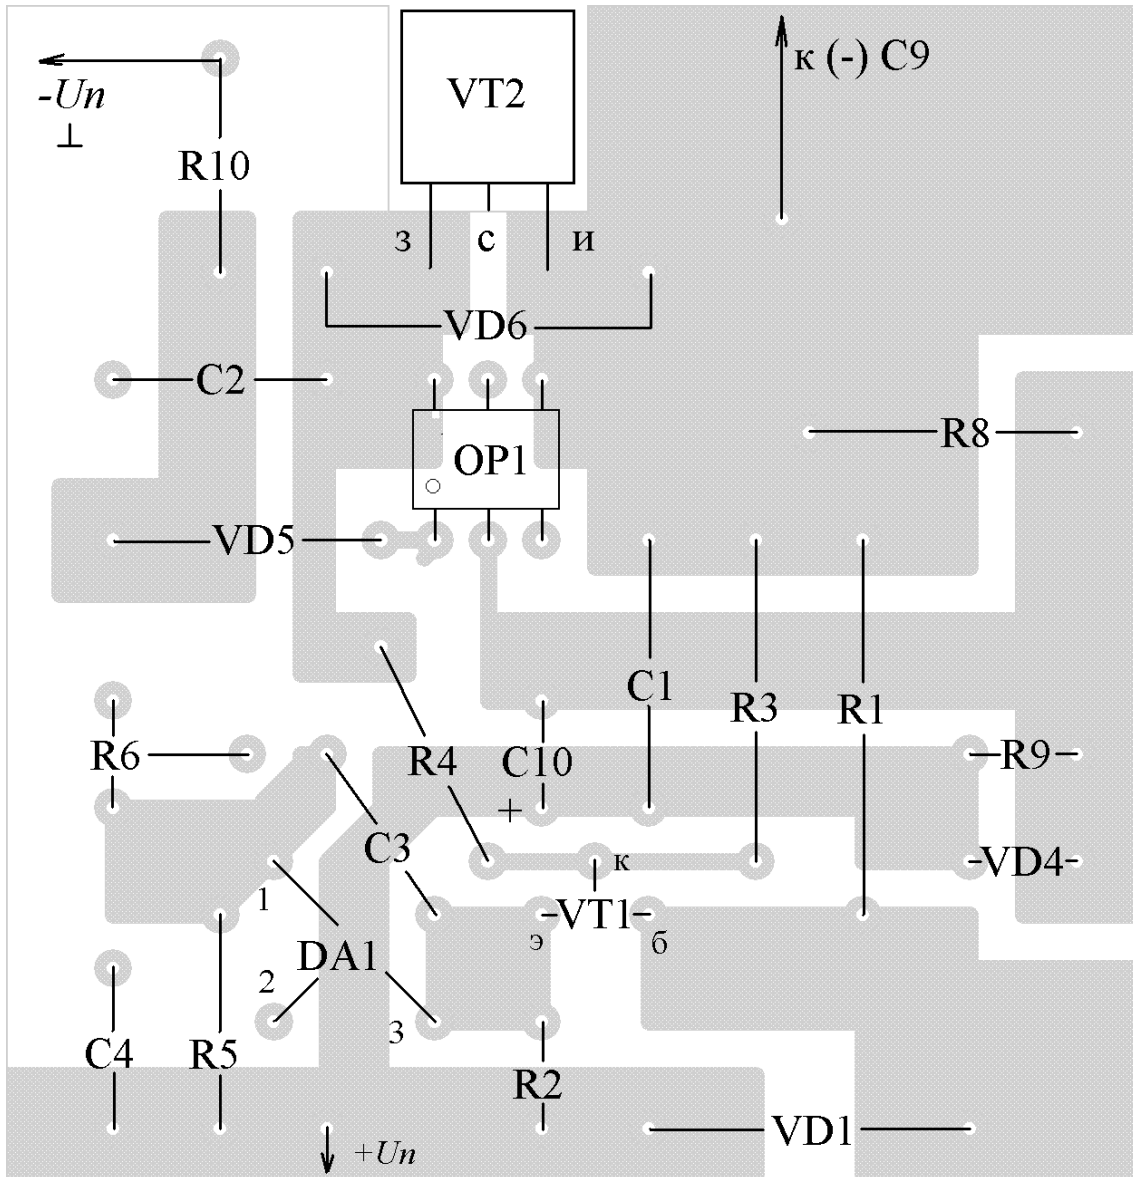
Эскиз расположения деталей на монтажной плате стабилизатора
